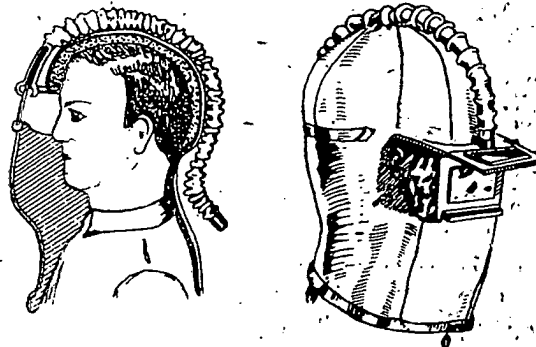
Шлем для сварщика с подачей свежего воздуха
